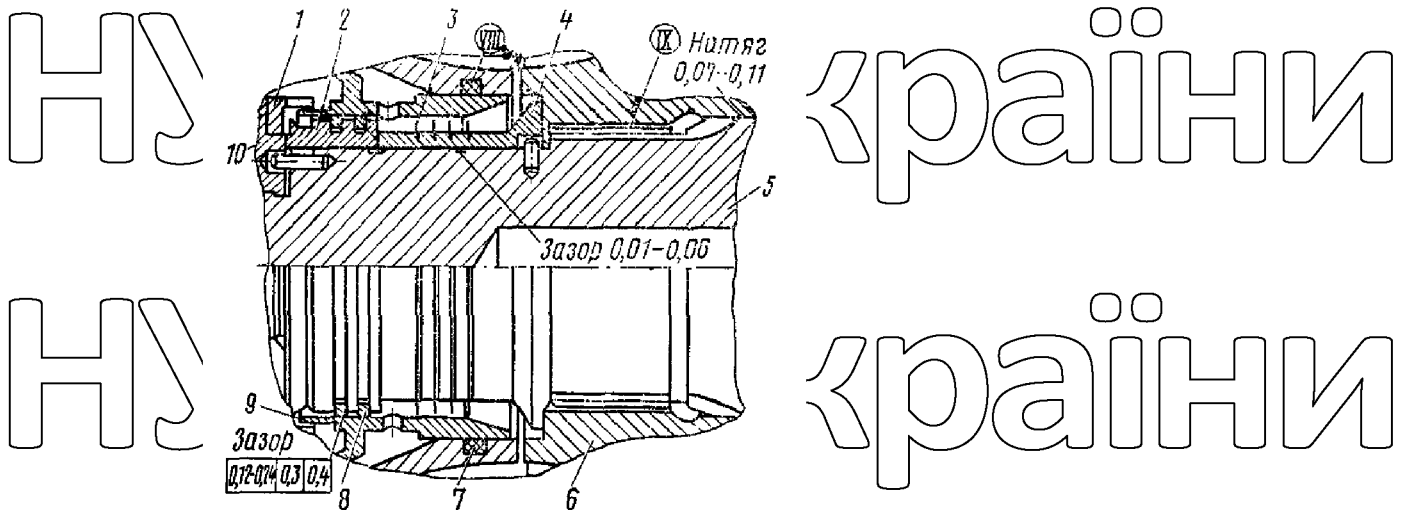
Вузол ущільнення турбокомпресора: 1-імплер; 2-втулка; 3-стрічка; 4-втулка ущільнення; 5-вал ротора; 6-колесо компресора; 7-гумова кільце; 8-ущільнювальне кільце; 9-обойма; 10-плата
